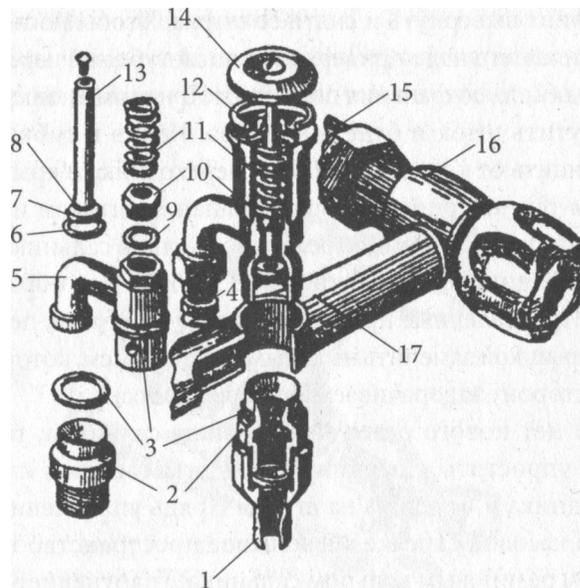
Смеситель с вертикально расположенным кнопочным переключателем: 1 — излив; 2 — переходник; 3 — уплотнительное резиновое кольцо; 4 — гибкий шланг; 5 — угольник; 6 — нижнее резиновое кольцо; 7 — верхнее резиновое кольцо клапана; 8 — пластмассовый клапан; 9 — резиновый сальник; 10 — втулка сальника; 11 — пружина; 12 — кнопка; 13 — шток; 14 — колпачок; 15 — патрубок; 16 — корпус; 17 — основание
